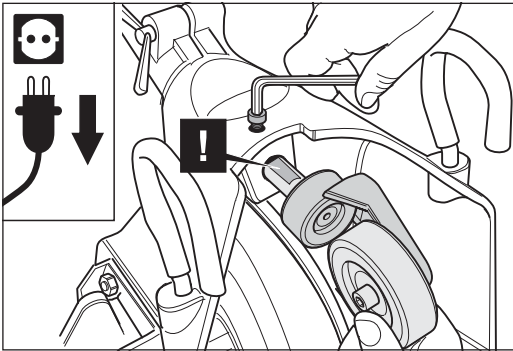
Die Klemmschraube lösen und das komplette Hinterrad aus dem Maschinengehäuse ziehen. Beim Einbau die Spannfläche der Spornachse zur Schraube hin ausrichten.
